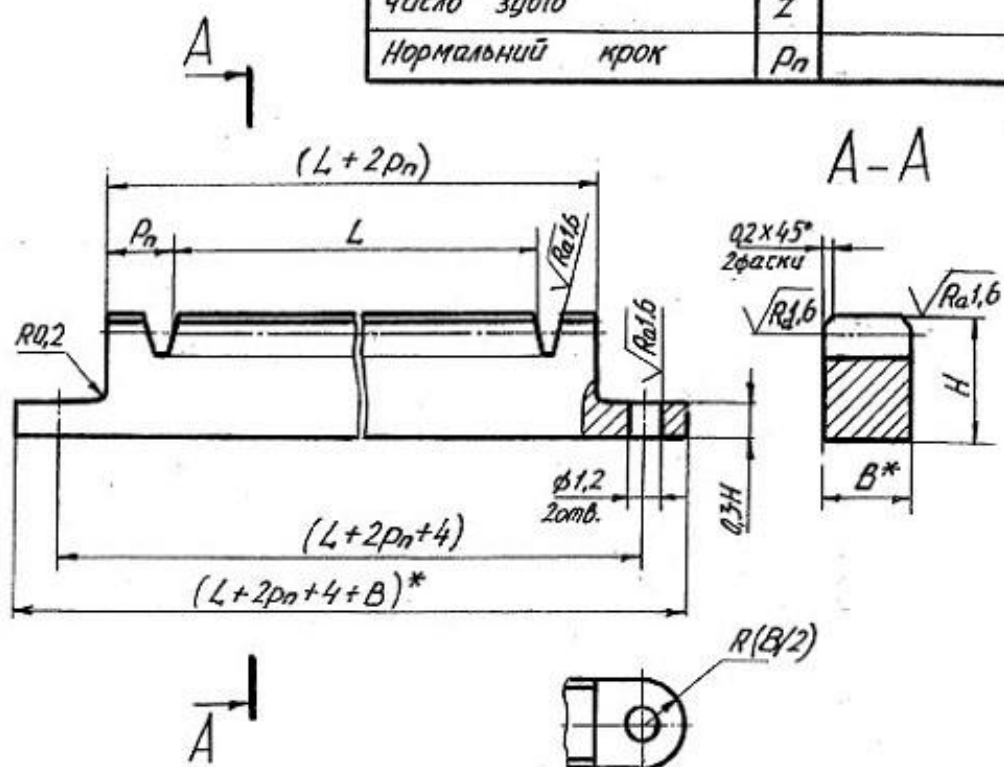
Кресленик рейкової зубчастої передачі
